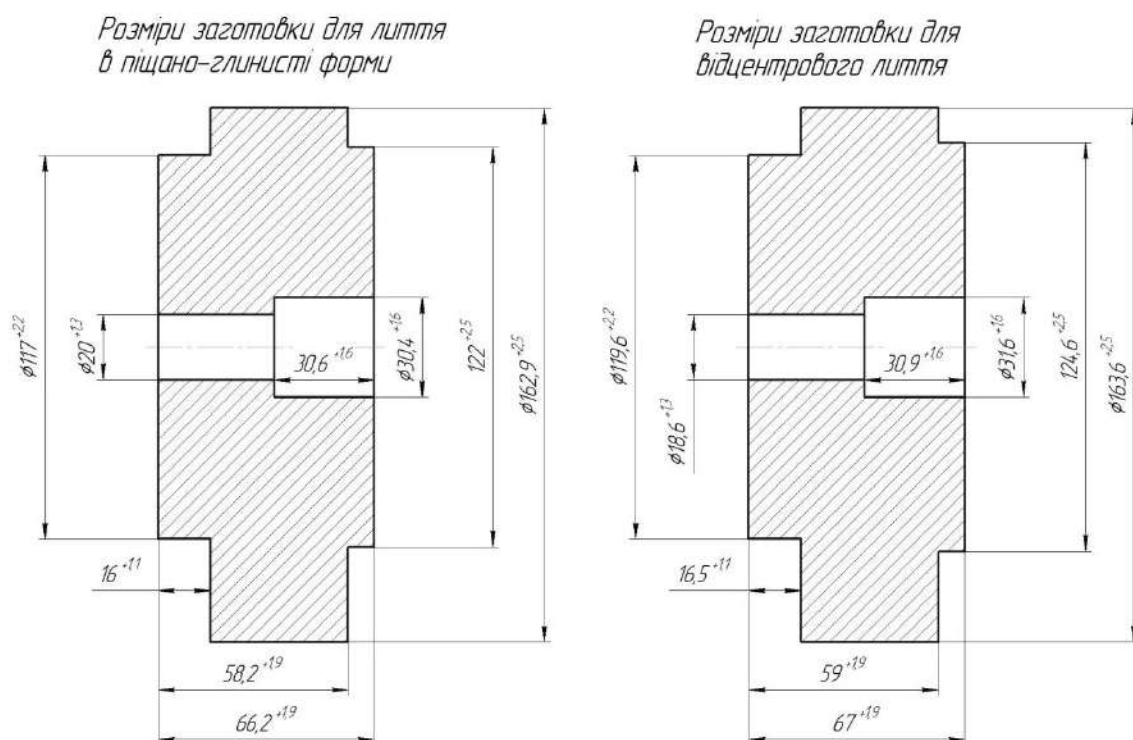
Ескіз заготовки для виготовлення литтям (ескіз для лиття в піщано-глинисті форми та відцентрового лиття)
